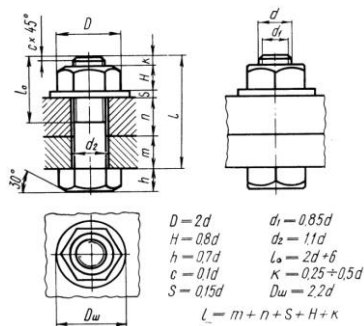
Чертеж болтового соединения:  $d$  – диаметр резьбы;
